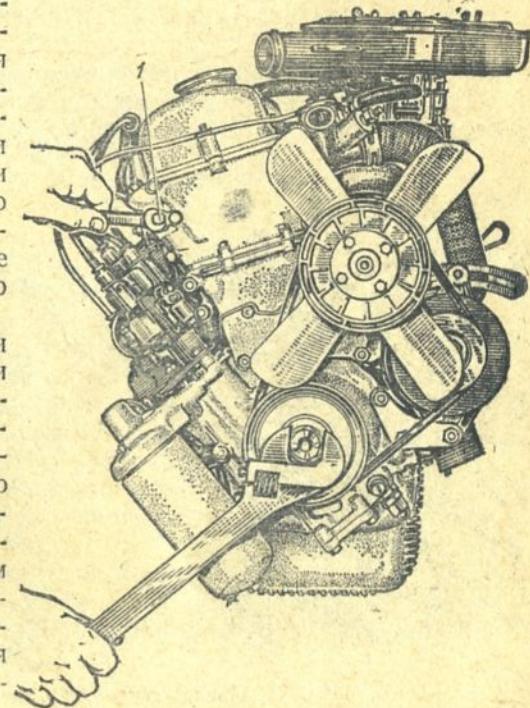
Регулировка натяжения цепи привода газораспределения:
